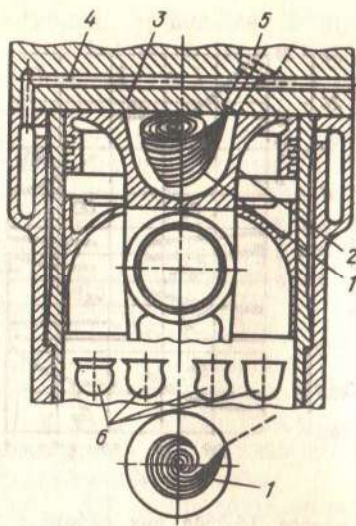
Схема смесеобразования в дизеле фирмы «Elko»: 1 — форма топливного факела; 2 — поршень с поверхностью скольжения в зоне выше уплотнительного пояса; 3 — головка цилиндра; 4 — сверление для охлаждения форсунки; 5 — форсунка; 6 — формы КС в поршне для процесса смесеобразования с однодырчатой форсункой
